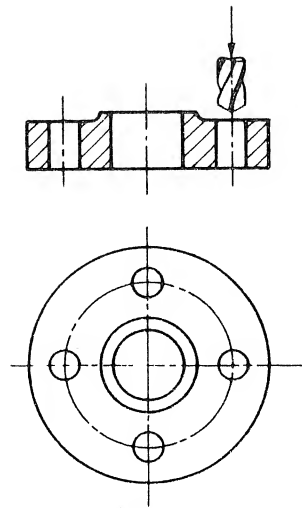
Mecanizado de un conjunto de agujeros auxiliares.
